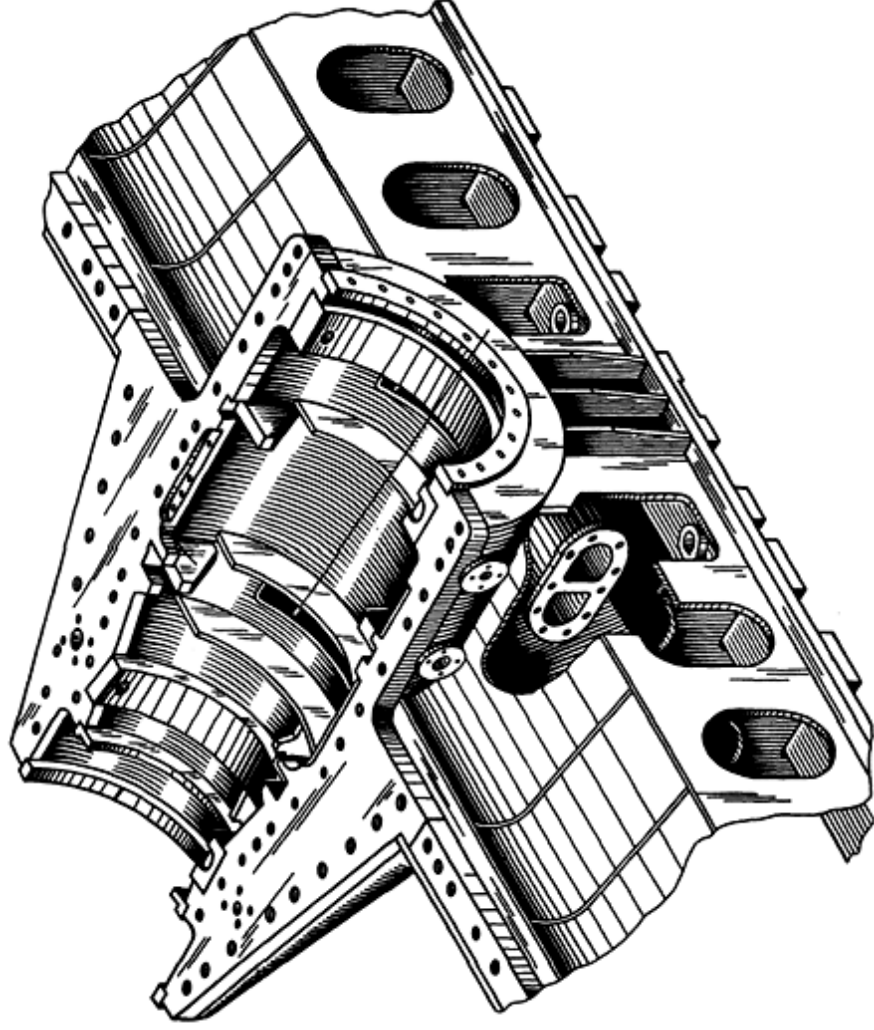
Корпус встроенных подшипников (картер подшипников)
